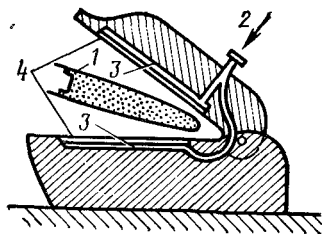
Приспособление с двухсторонним давлением для склеивания рулей и элеронов:
